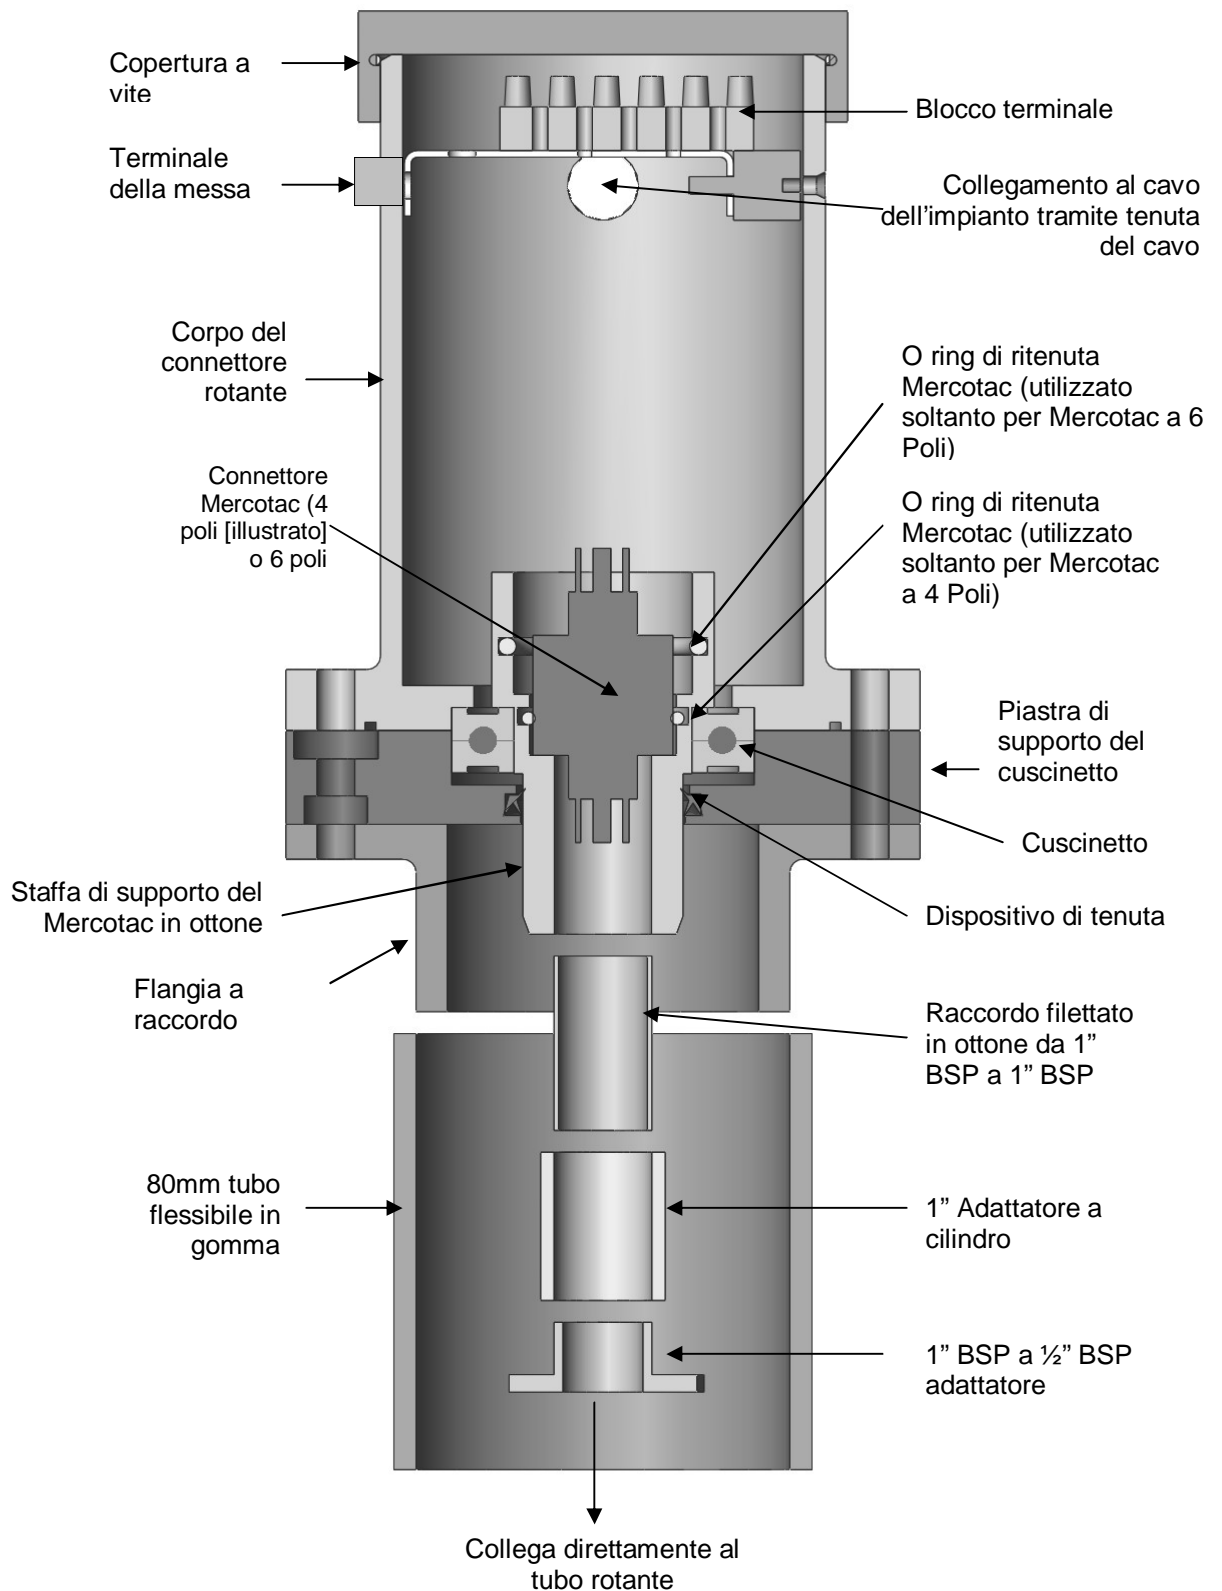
Tipo 'C' assemblaggio del connettore rotante
